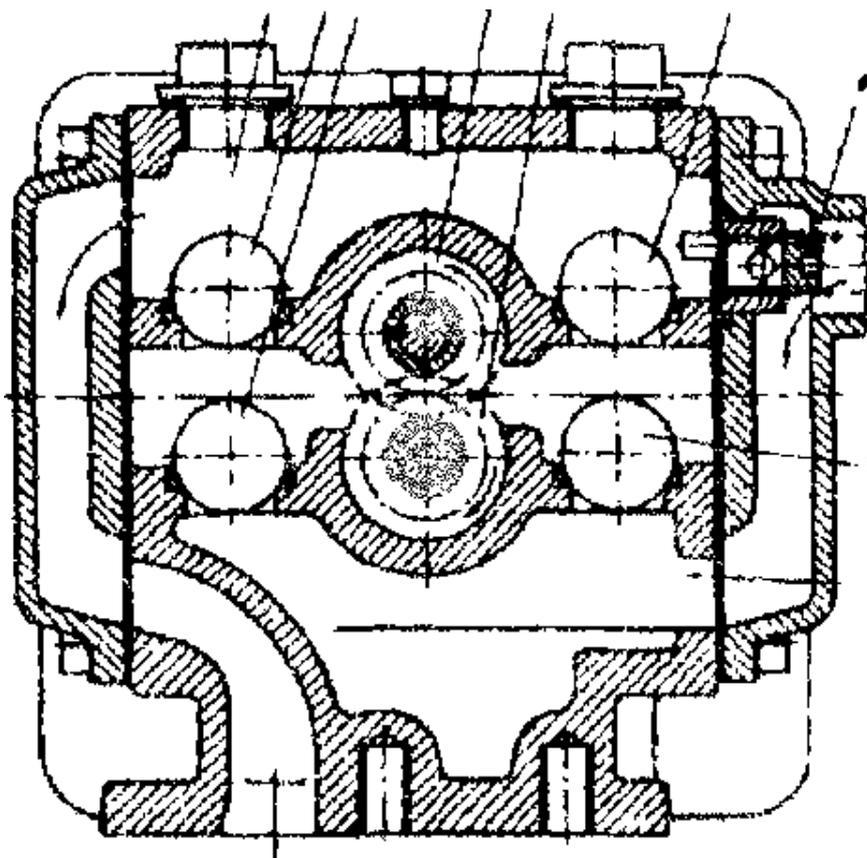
Шестеренчатый реверсивный насос дизеля NVD-36
